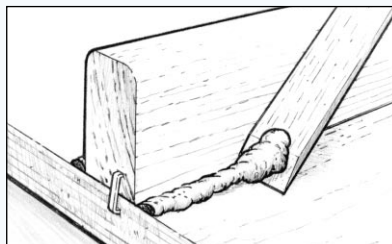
Retirer ou façonner l'excédent d'époxy qui s'échappe de la jointure.
